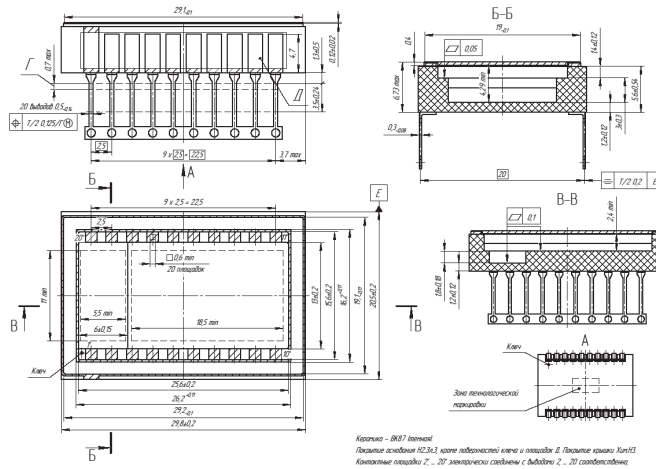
Габаритные, установочные и присоединительные размеры корпуса МК 2155.20-1
